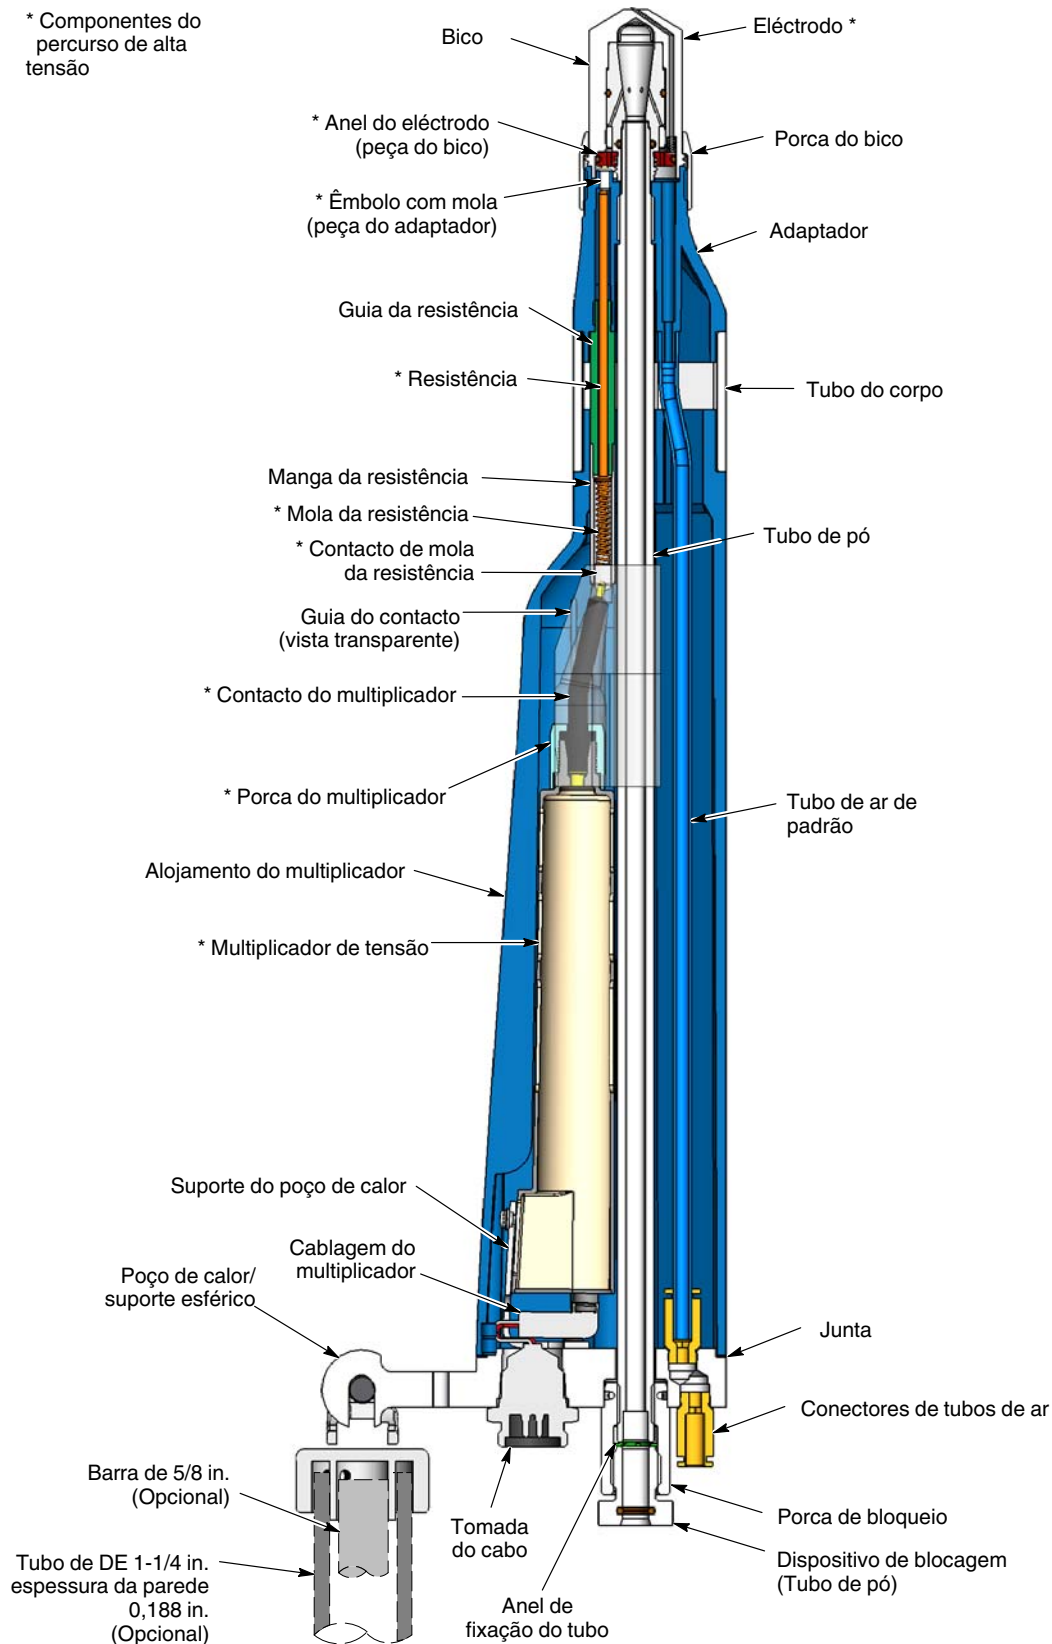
Vista em corte - Componentes e montagem da pistola com barra de suporte
